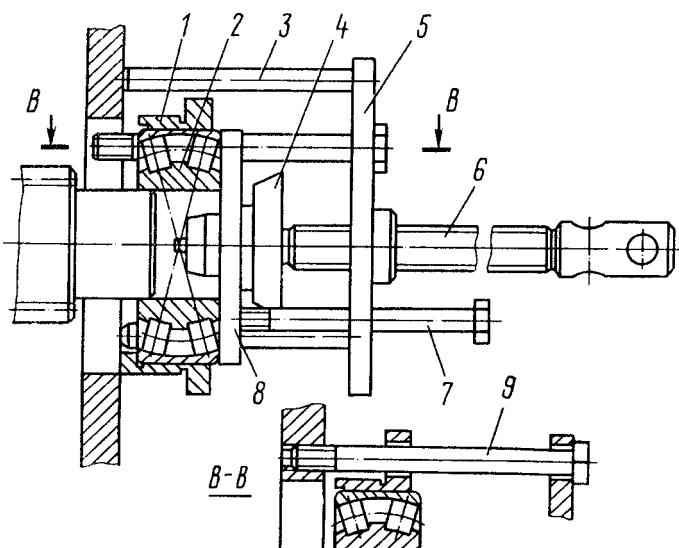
Приспособление для установки заднего подшипника промежуточного вала:
